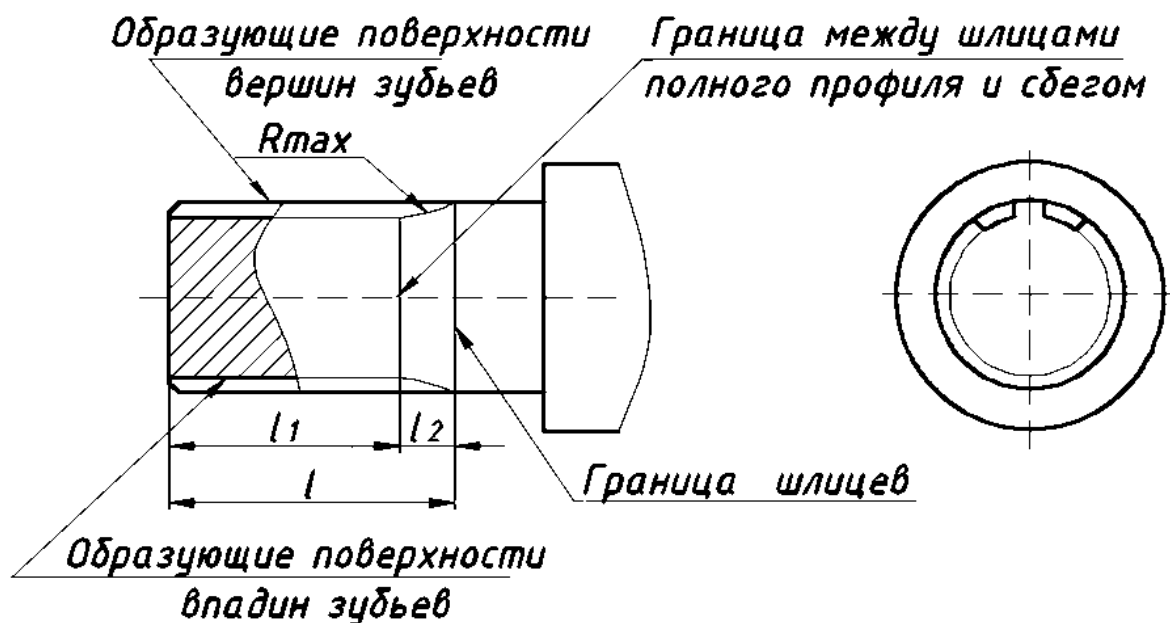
Образец условного изображения шлицев: l – полная длина зубьев; l_1 – длина зубьев полного профиля; l_2 – длина сбегом; R_{max} – наибольший радиус инструмента (фрезы)
